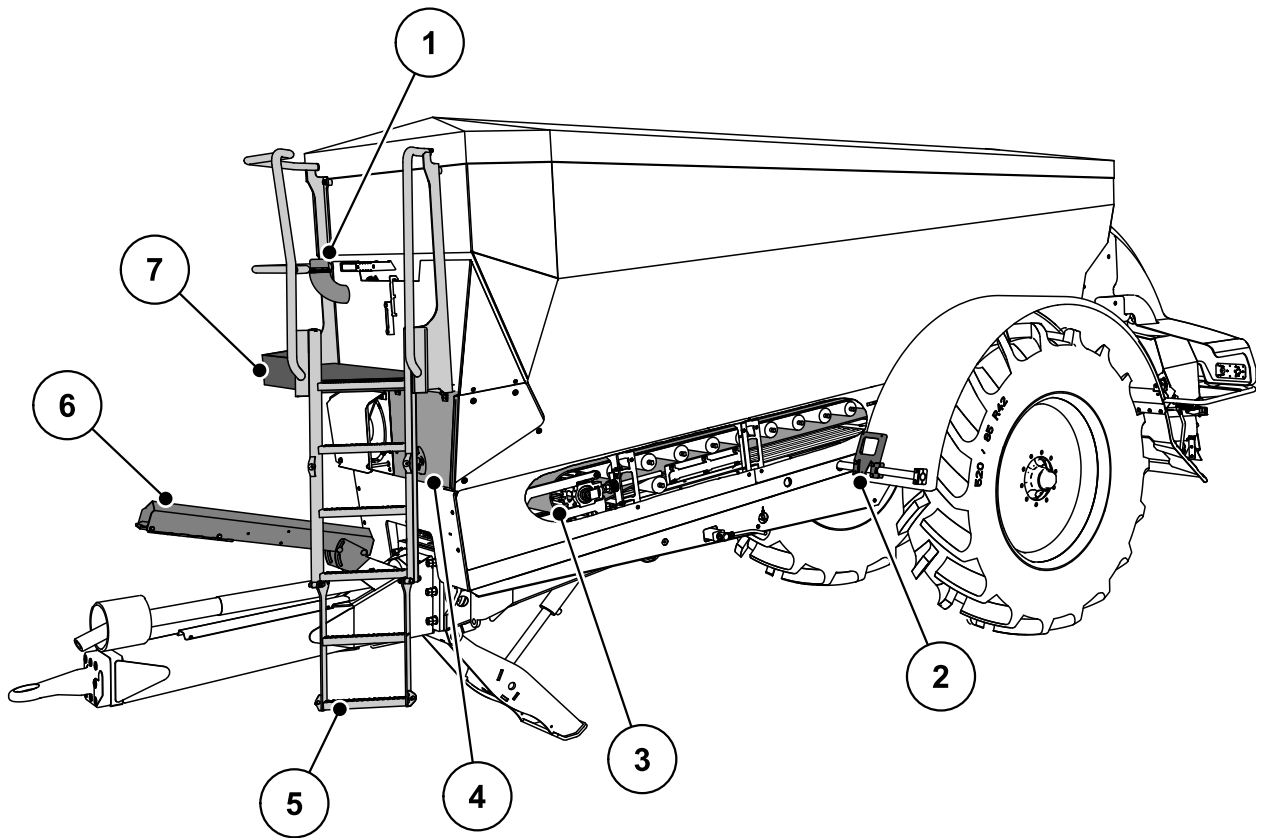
Composants et fonctionnement de la machine AXENT, vue avant
